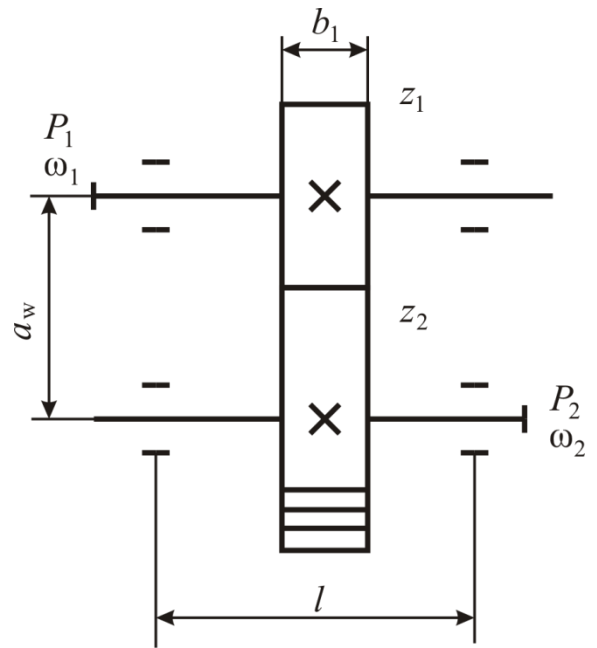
Схема открытой цилиндрической прямозубой передачи
